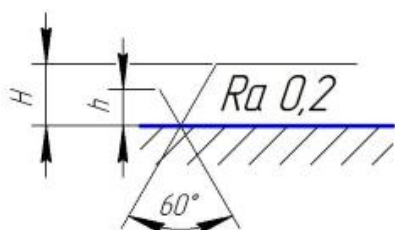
Структура обозначения шероховатости поверхности
